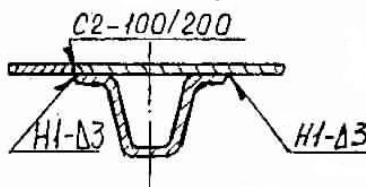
Приварювання нижньої кромки нового листа обшивки
